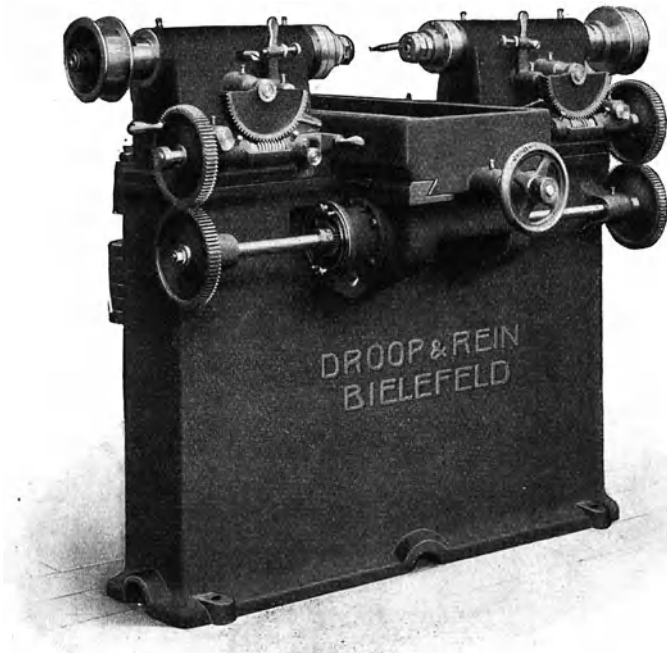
Die Keillochfräsmaschine von Droop & Rein.
